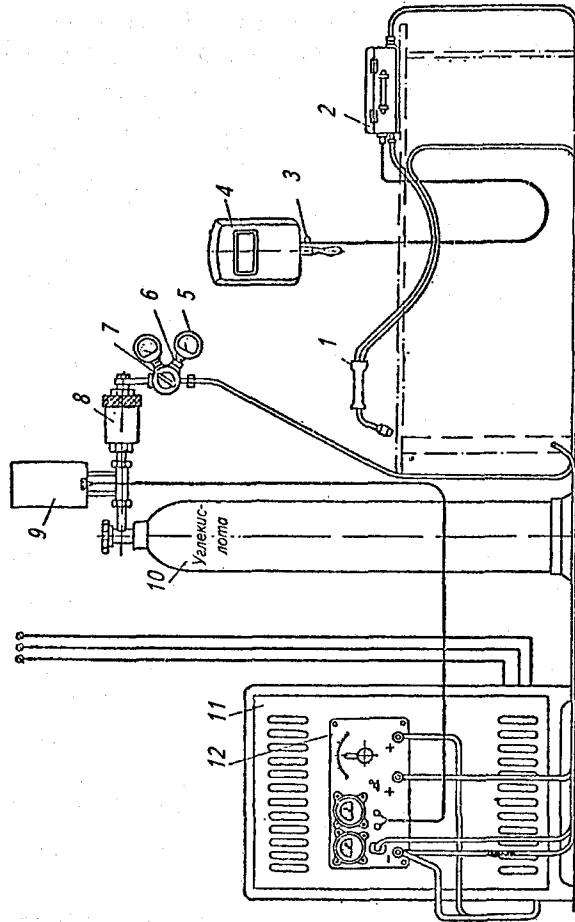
Схема поста полуавтоматической сварки тонкой электродной проволокой в углекислом газе: 1 — держатель; 2 — подающий механизм; 3 — кнопка включения; 4 — защитный щиток; 5 — манометр на 6 ат.; 6 — переходной штуцер для установки манометра; 7 — редуктор кислородный с манометром высокого давления; 8 — осушитель газа; 9 — подогреватель газа; 10 — баллон с углекислым газом; 11 — сварочный выпрямитель (либо генератор); 12 — пульт управления
